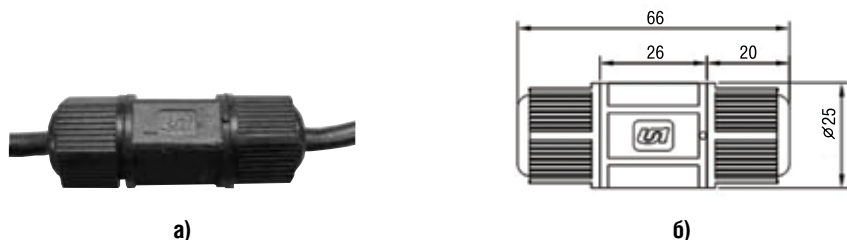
Герметичный соединитель CJ-04-х: а) внешний вид; б) чертеж
